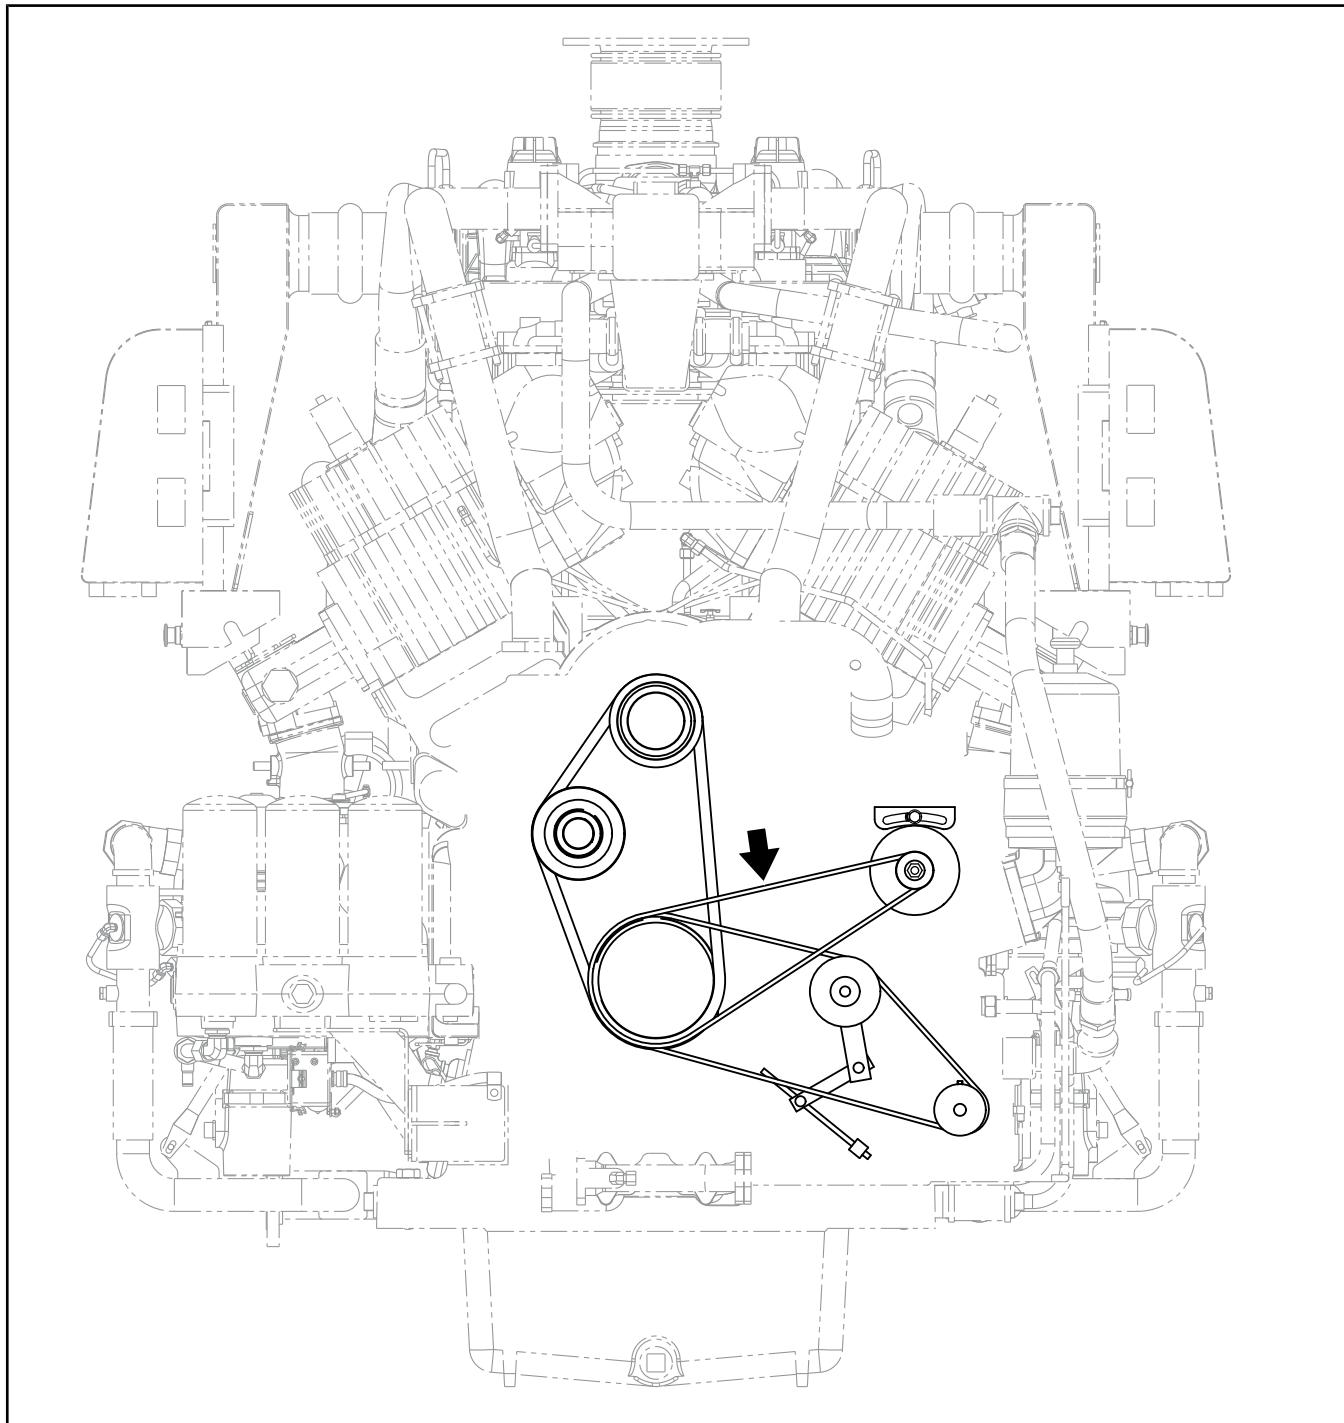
Место измерения натяжения ремня генератора переменного тока
